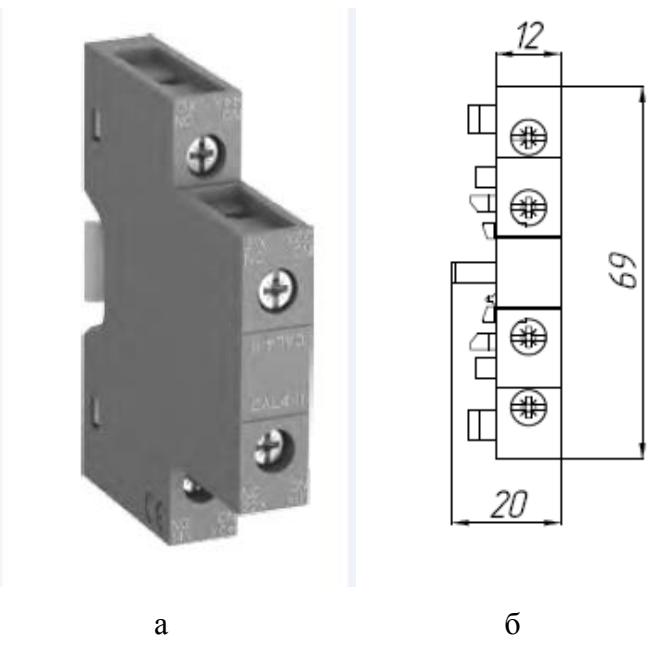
Общий вид (а) и габаритные размеры (б) дополнительного контактного блока CAL4-11.
